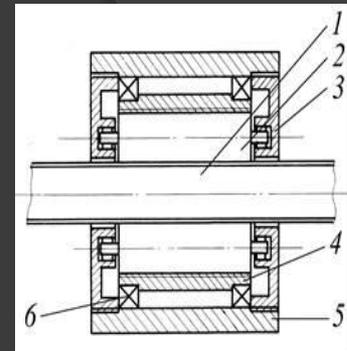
Передача винт – неподвижное водило с резьбовыми роликами с кольцевой нарезкой – гайка с кольцевой нарезкой: 1 – винт; 2 – резьбовые ролики; 3 – водило; 4 – гайка; 5 – корпус; 6 – подшипники
